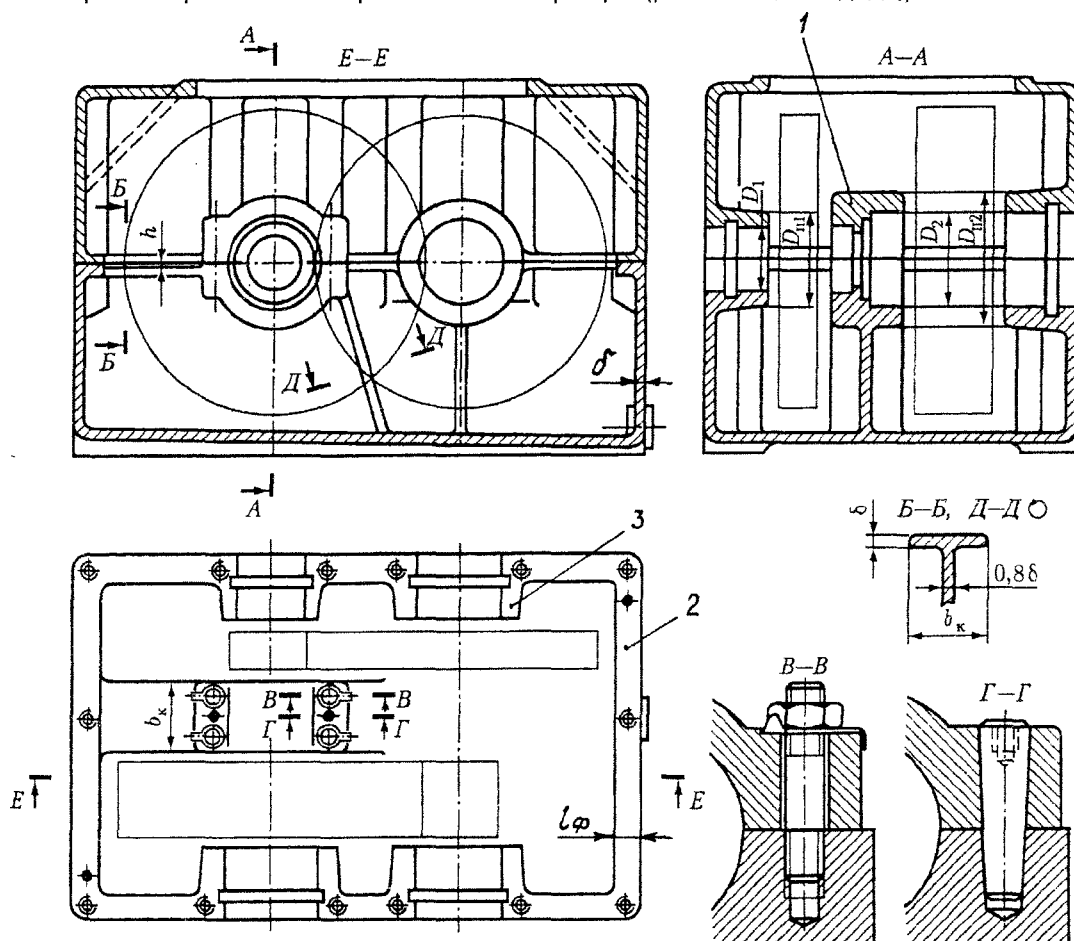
Двухступенчатый цилиндрический горизонтальный соосный редуктор с внутренней стенкой ограниченной длины [2]: 1 – промежуточная опора; 2 – фланец корпуса; 3 – прилив для подшипникового гнезда
